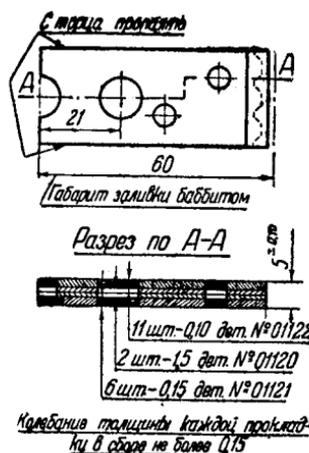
Дет. № 01119. Прокладка крышки уплотнения в сборе
